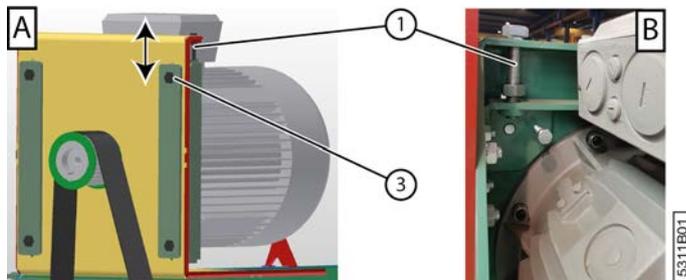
Vue avant [A] et vue arrière détaillée [B] du moteur électrique
